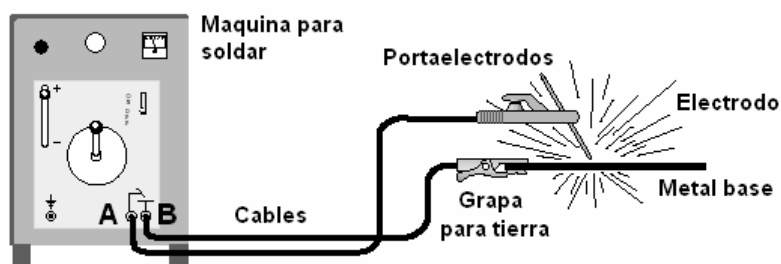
Equipo básico de soldadura con arco eléctrico.
